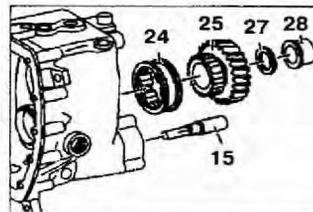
Снимите рычаг включения 15. Снимите шестерню 25, муфту включения 24 и упорную прокладку 27 из корпуса коробки передач. Снимите внутреннее кольцо подшипника 28.
